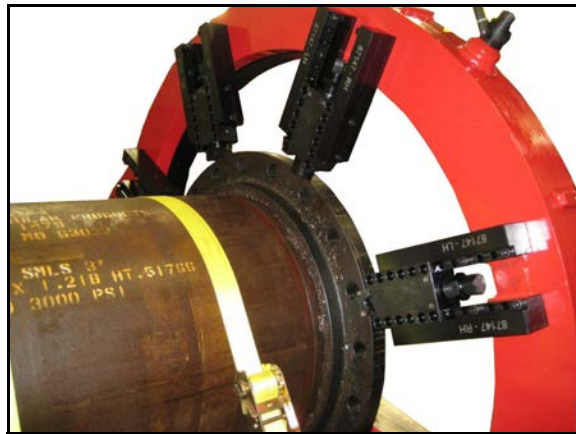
PIE DE EXTENSIÓN INSTALADO
